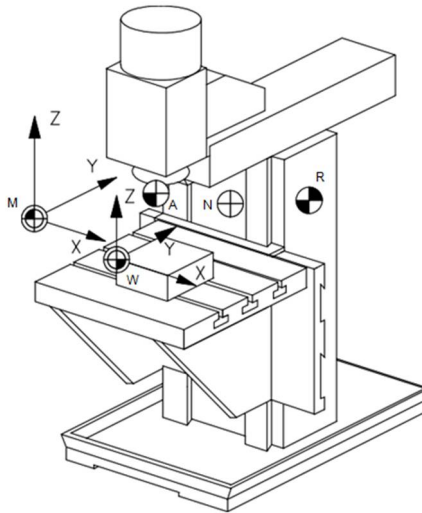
Встановлення нульової точки заготовки на вертикально фрезерному верстаті з ЧПК
